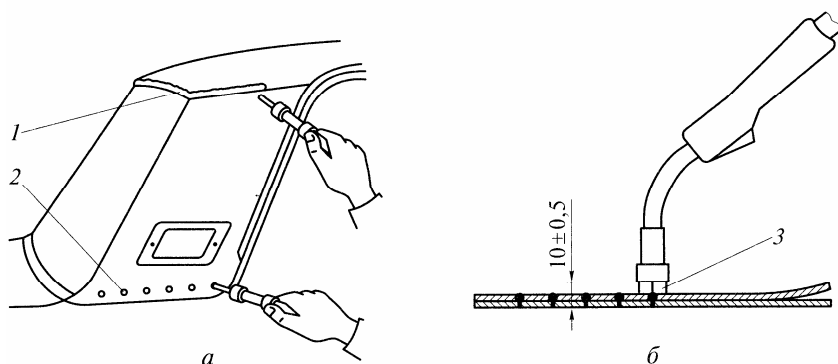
Способы сварки (а) и установка горелки при точечной сварке по отверстиям (б): 1 – сварка сплошным швом; 2 – сварка внахлестку по отверстиям; 3 – опорные ножки газового сопла
